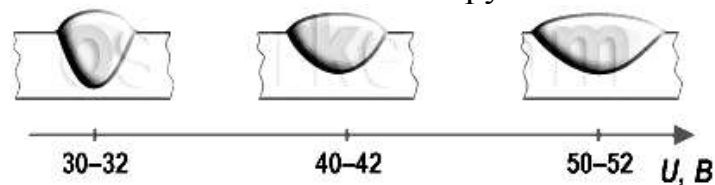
Вплив напруги дуги на форму й розміри зварного шва
